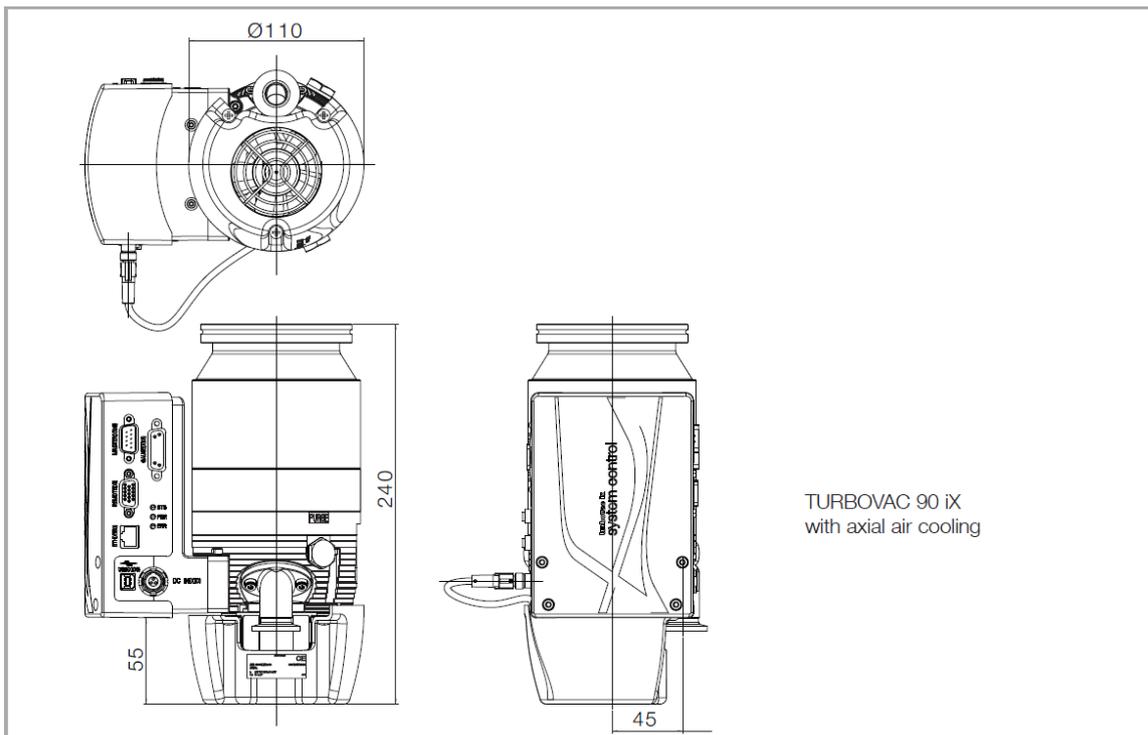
TURBOVAC 90 i 尺寸图 (轴向风扇)
